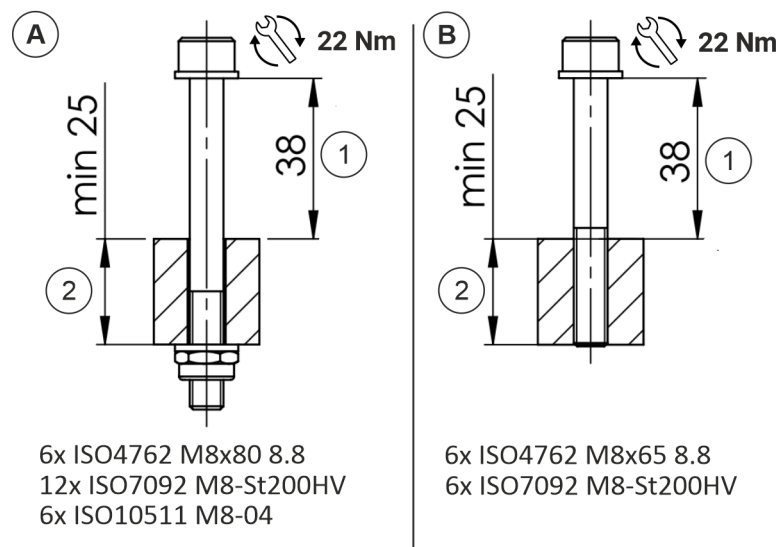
Verschraubung der Roboterbasis (Befestigungselemente)
